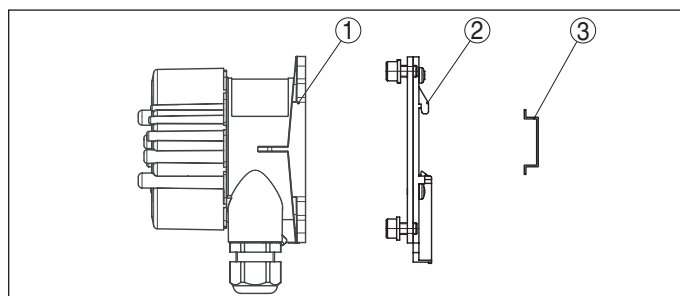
VEGADIS с корпусом из алюминия или нержавеющей стали, для монтажа на несущей рейке
